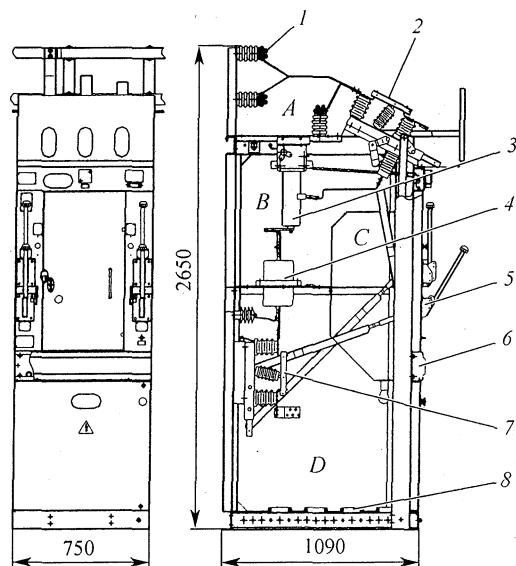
Устройство камеры КСО-2001 МЭШ с вакуумным выключателем ВВ/TEL: *A* — отсек сборных шин; *B* — высоковольтный отсек; *C* — релейный отсек; *D* — кабельный отсек; 1 — сборные шины; 2 — шинный разъединитель; 3 — вакуумный выключатель; 4 — трансформаторы тока; 5 — приводы; 6 — клеммник; 7 — линейный разъединитель; 8 — трансформатор тока нулевой последовательности
